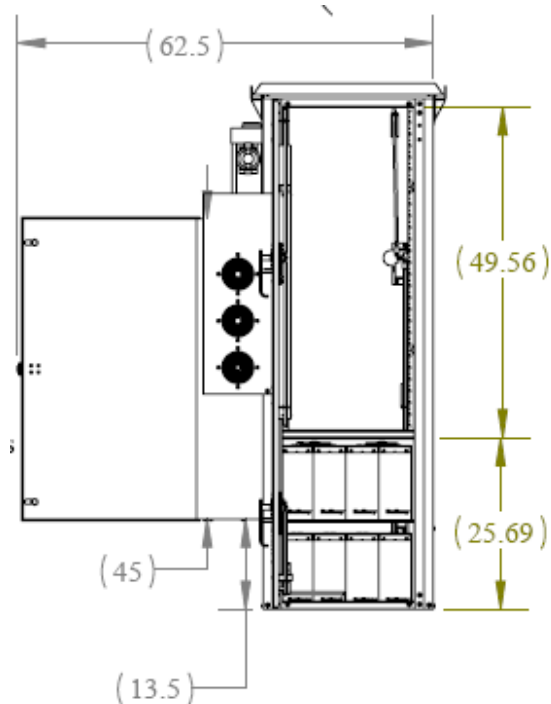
VISTA DIMENSIONAL FRONTAL DEL LTEE-A
